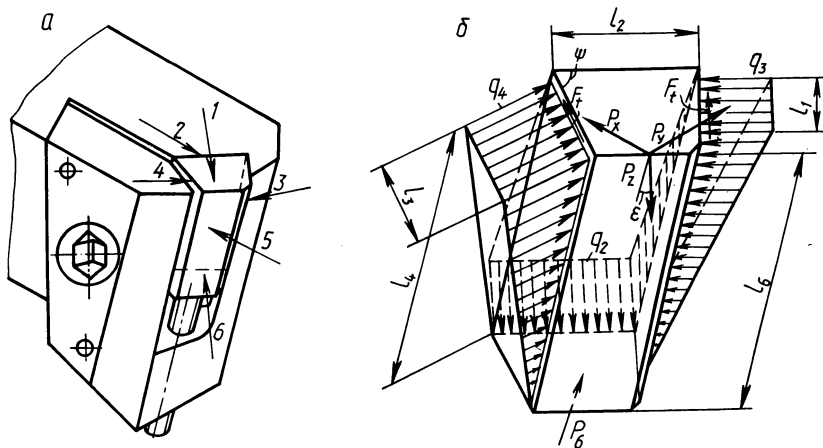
Сборный токарный резец: а – общий вид; б – схема распределения контактных нагрузок на опорных поверхностях пластины.
